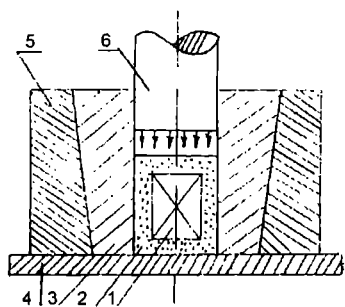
Прессформа горячего прессования с разъемными вкладышами
